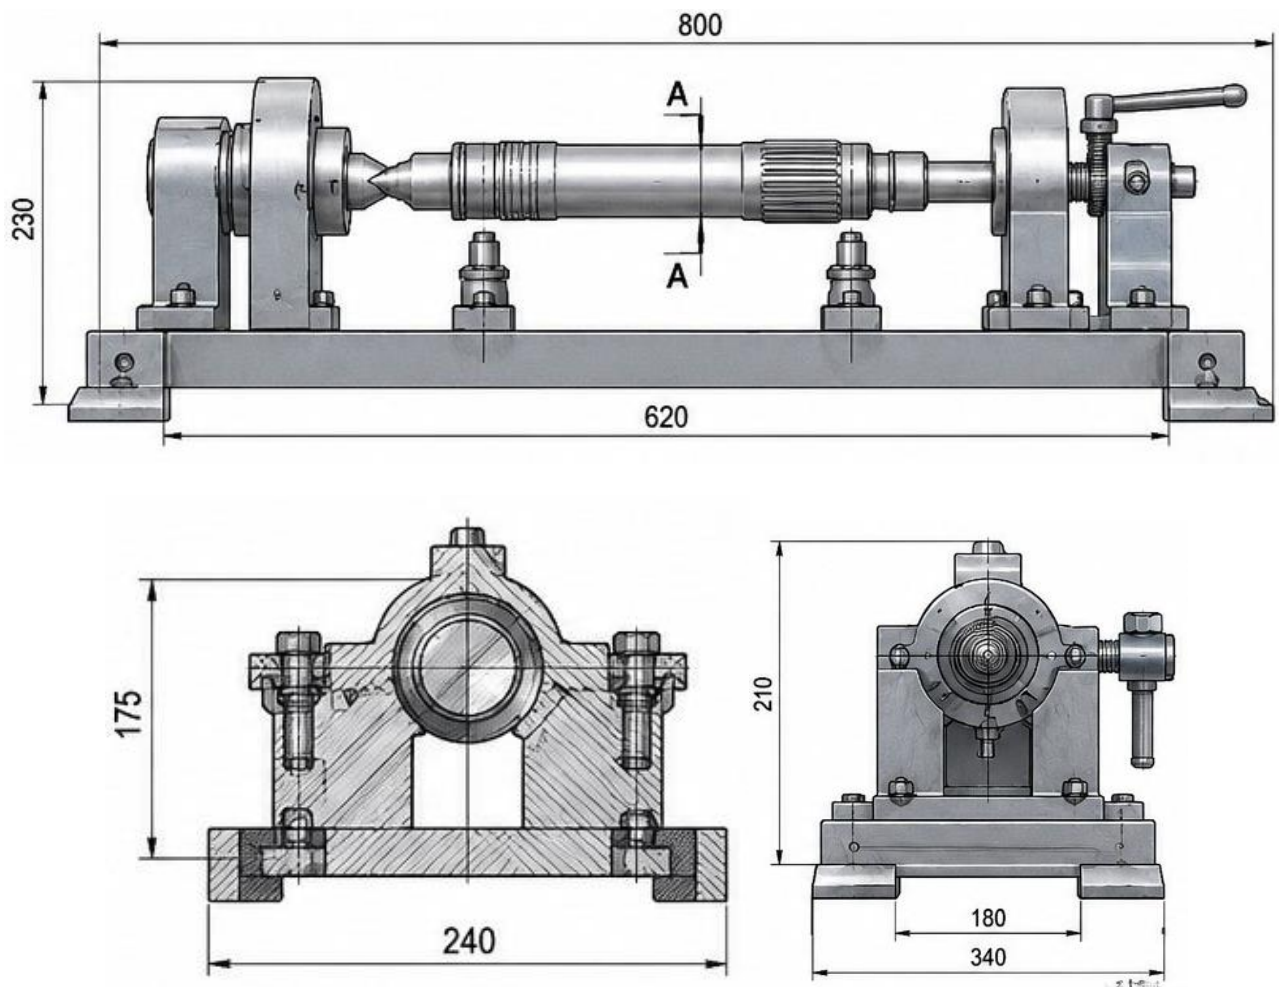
Пристосіблення для базування та обробки валу
